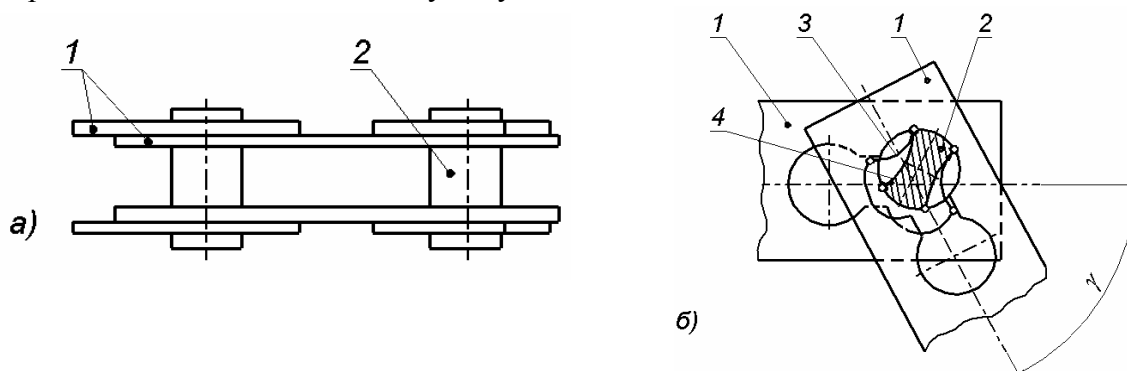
Схеми конструкції пластинчастого тягового ланцюга двостороннього повороту (а) та взаємодії шарніра тертя кочення ланцюга з двостороннім поворотом ланок ланцюга (б): 1 – пластина; 2 – валик; 3 – опукла робоча поверхня отвору пластини; 4 – увігнута робоча поверхня валика
